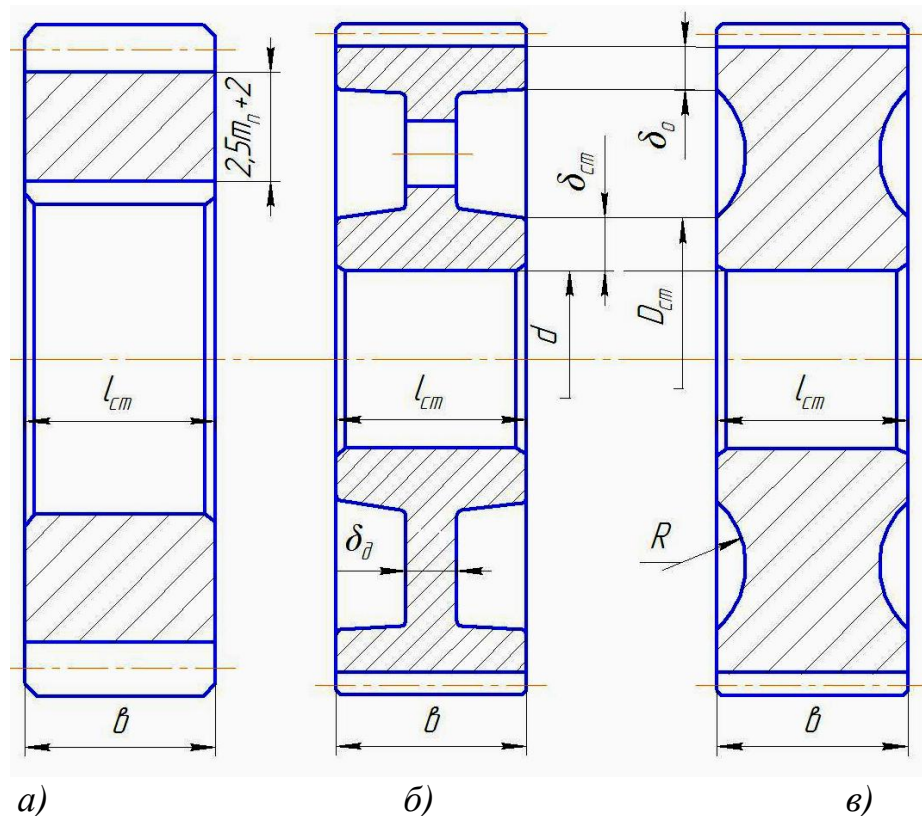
Типовые конструкции насадных цилиндрических колес
